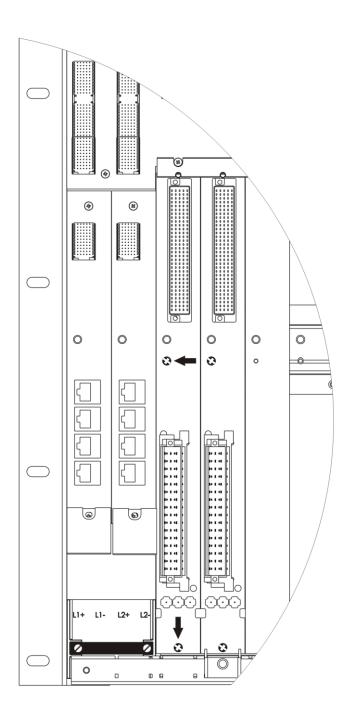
Festschrauben des mono Connector Boards, exemplarisch
